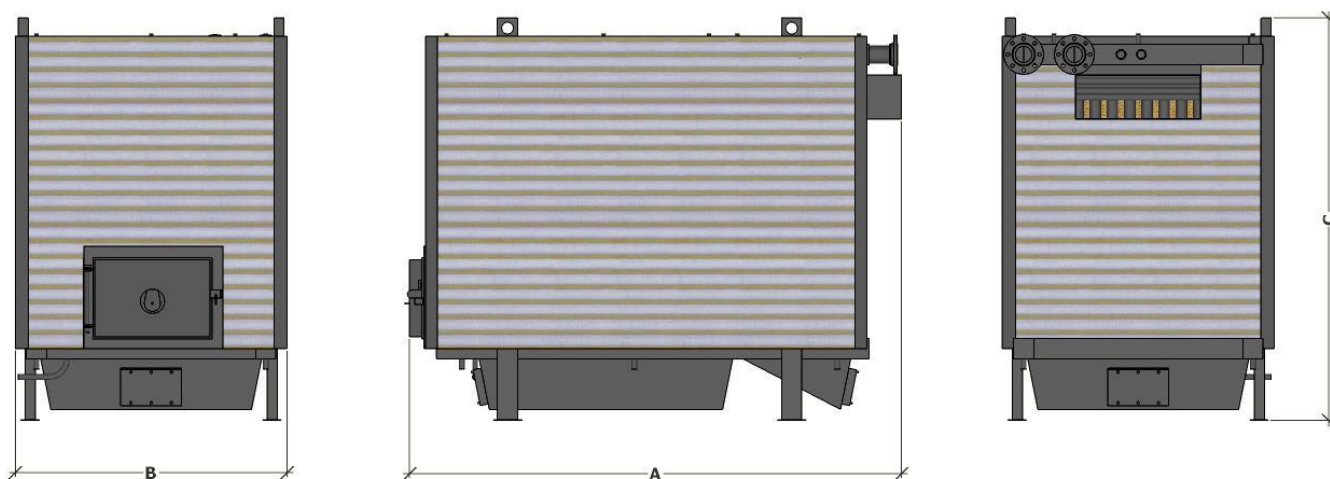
Устройство и габариты компоновки котла KVp-1.25
